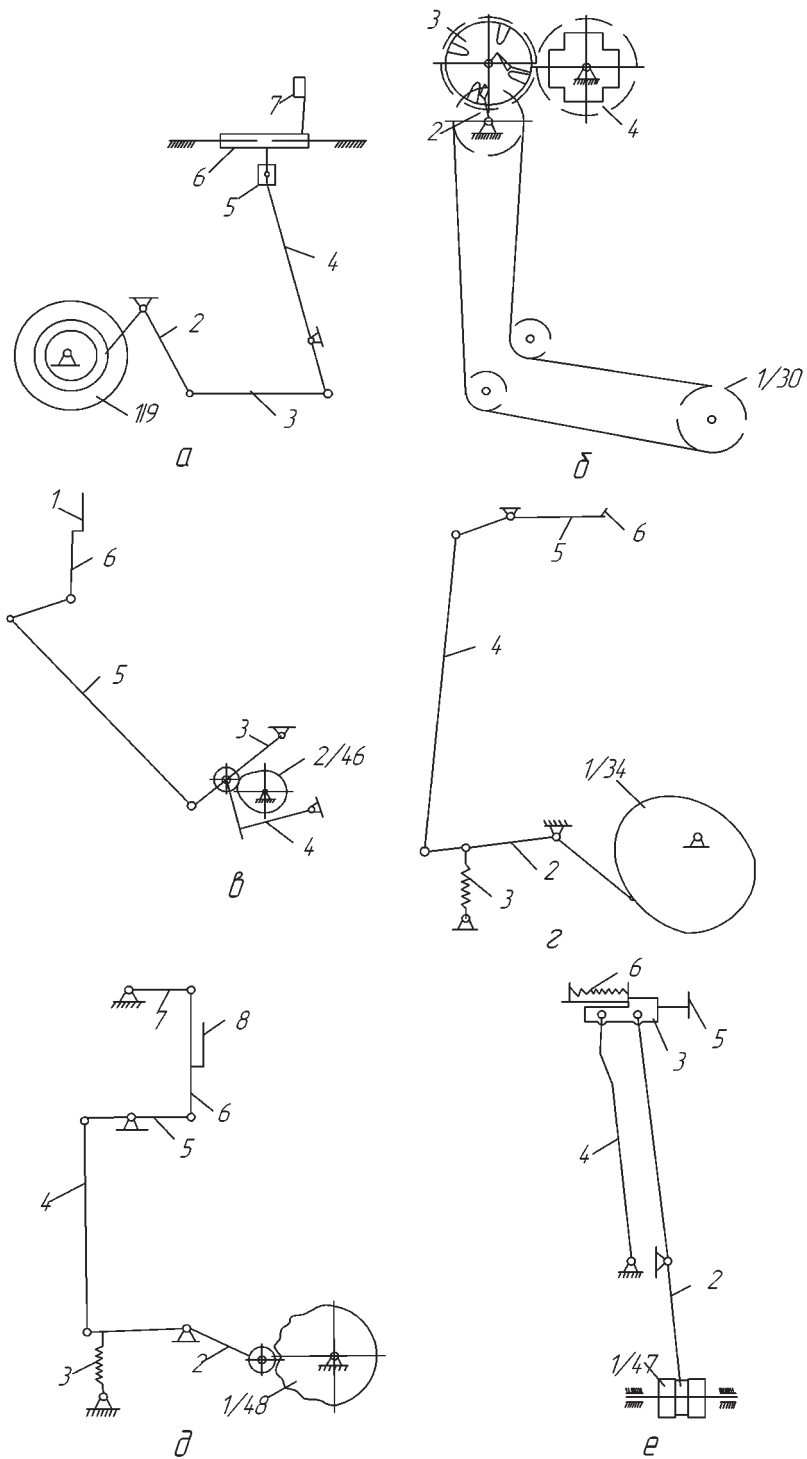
Механізми подачі пакета у дозатор, утрушування продукту в пакеті й передачі пакета в пакувальну карусель
